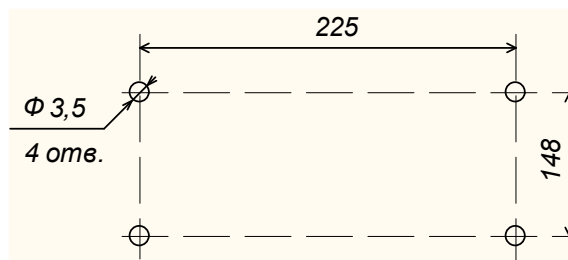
Размеры под сверление отверстий в панели для установки БАО
